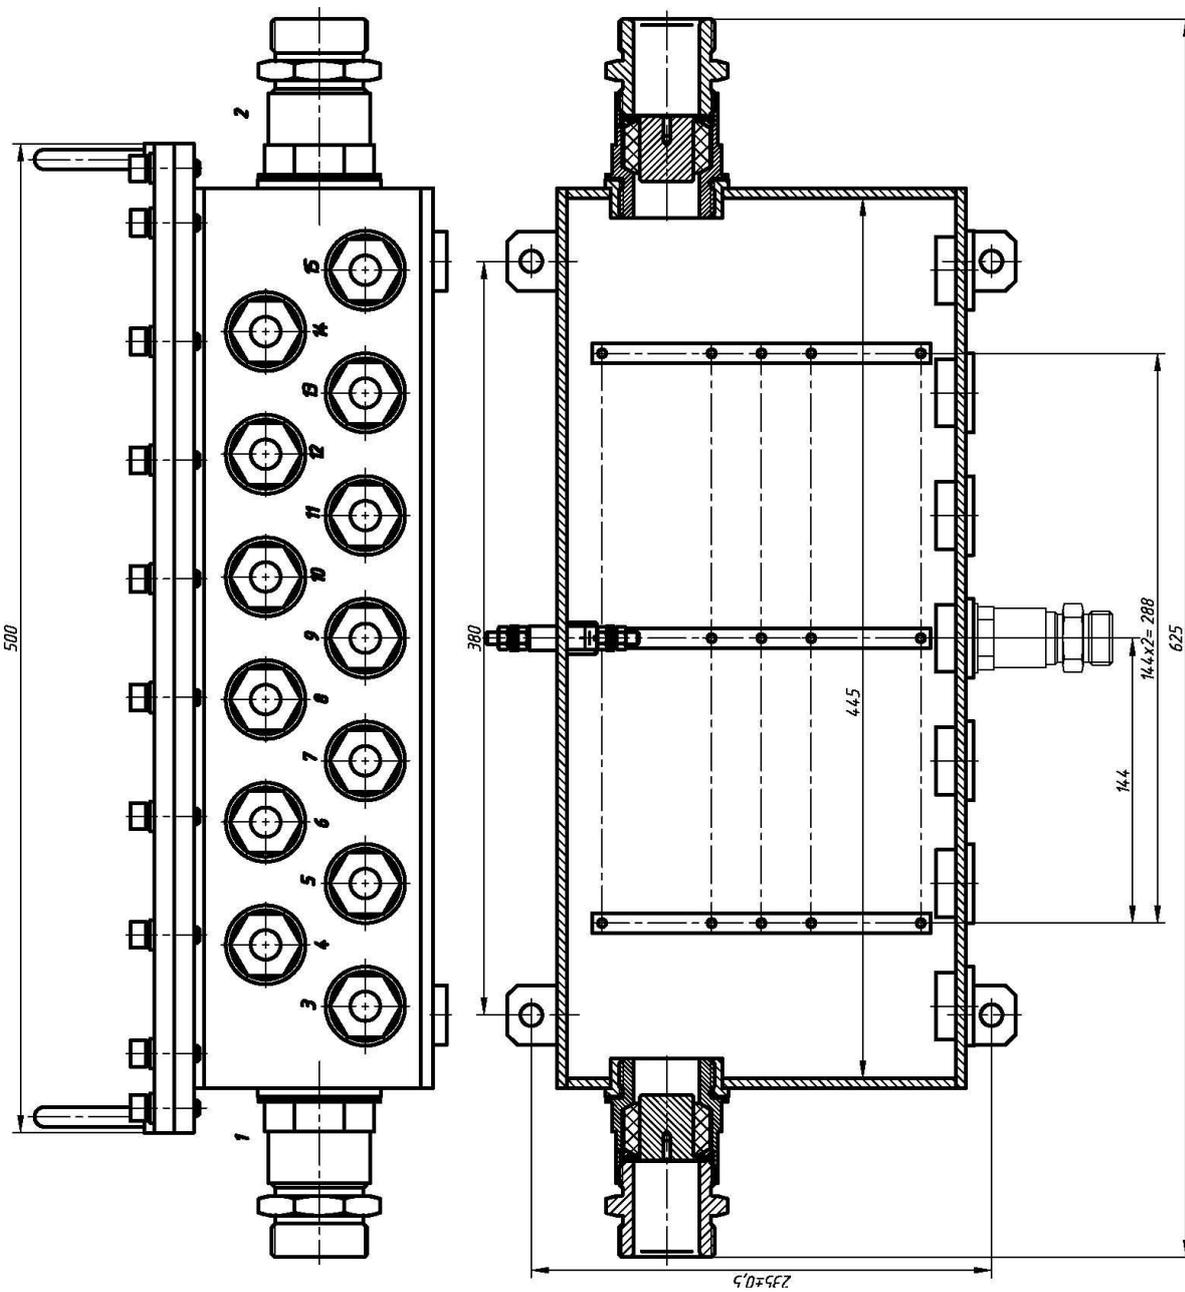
Габаритные, установочные и присоединительные размеры базовой коробки ExКСУВ-ПС500. Остальное смотреть рисунок В.1. По умолчанию в патрубках №№1 и 2 резьба G1 1/2, в патрубках №№ 3-15 резьба G3/4.
